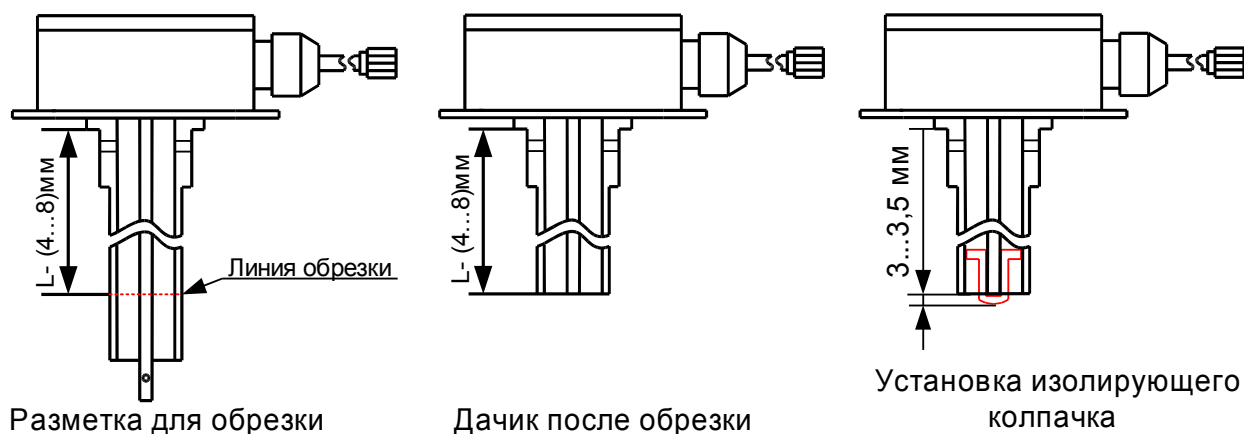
Разметка для обрезки, обрезка датчика до требуемой длины и установка изолирующего колпачка.
